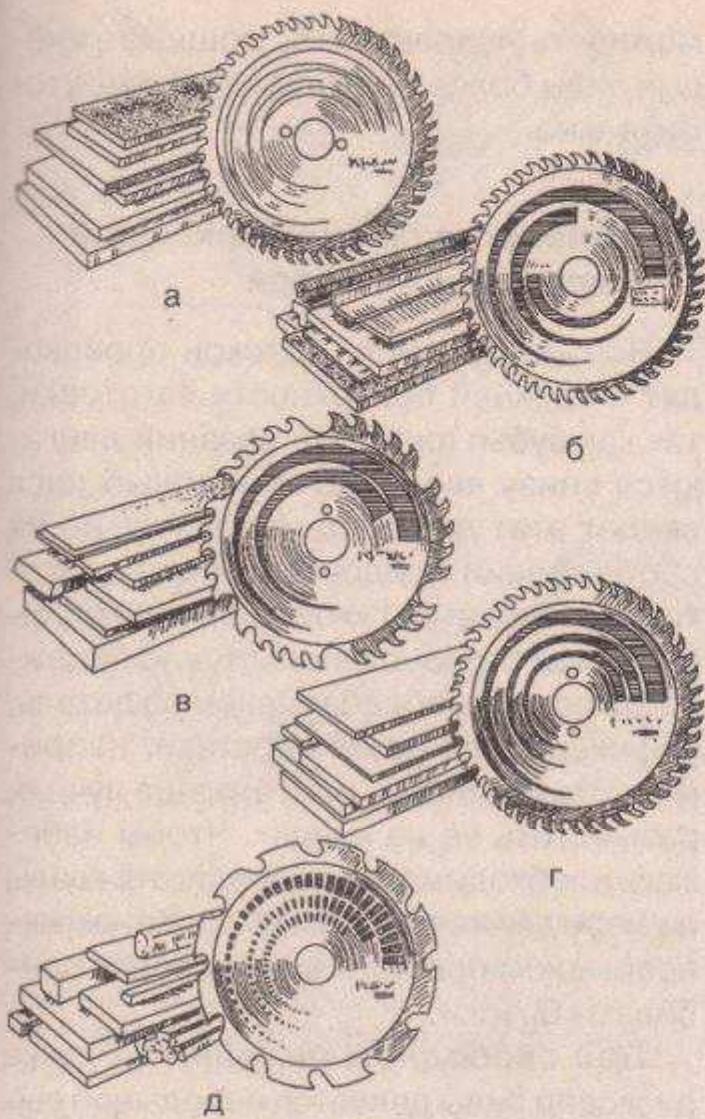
Диски: а — с остроконечными зубьями; б — с мелкими зубьями; в — с твердосплавными зубьями; г — со скошенными зубьями; д — с крупными зубьями
